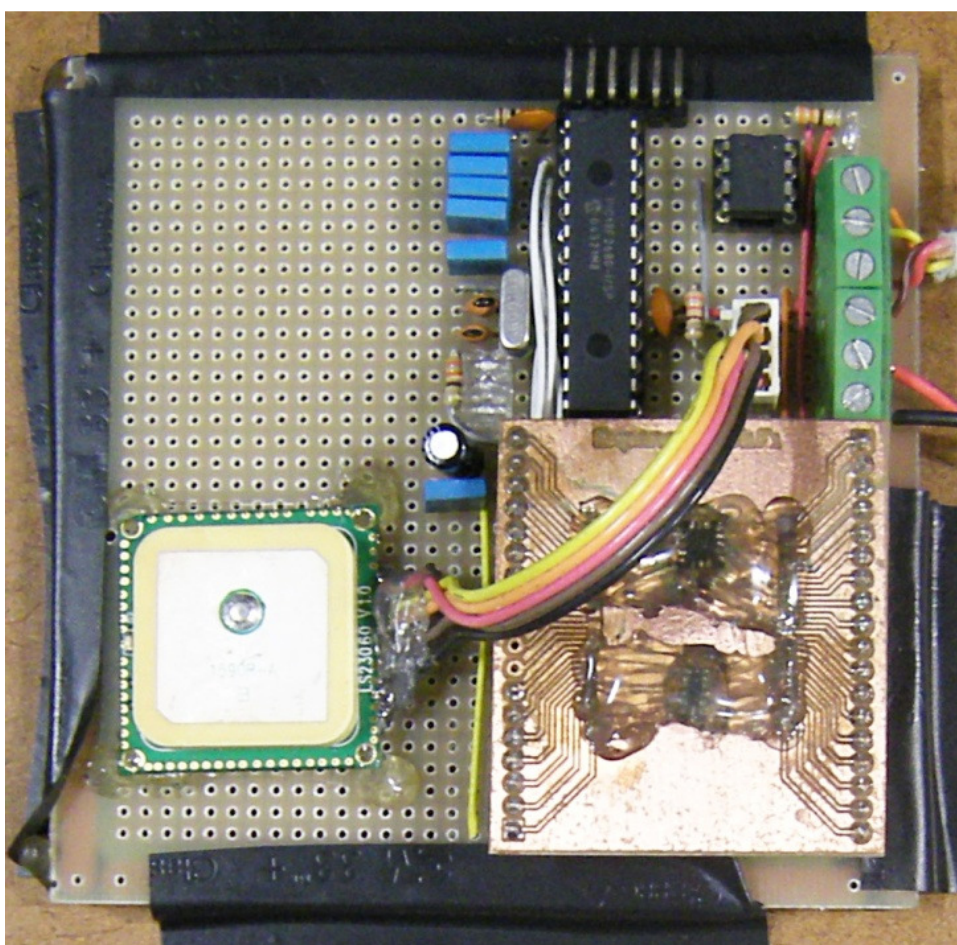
Hardware* montado em placa de circuito impresso universal.
